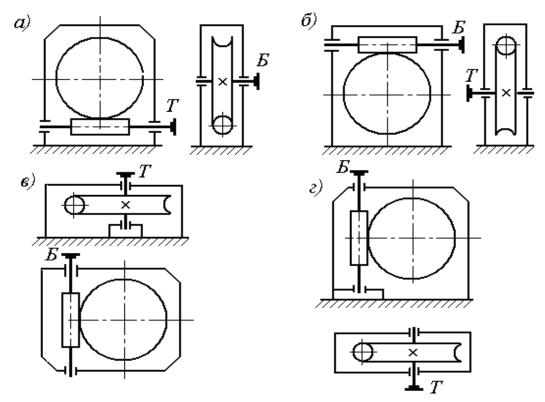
Кинематические схемы одноступенчатых червячных редукторов: с нижним (a) и верхним ( $\delta$ ) расположением червяка,  $\epsilon$  – с вертикальным расположением вала колеса,  $\epsilon$  – с вертикальным расположением вала червяка
